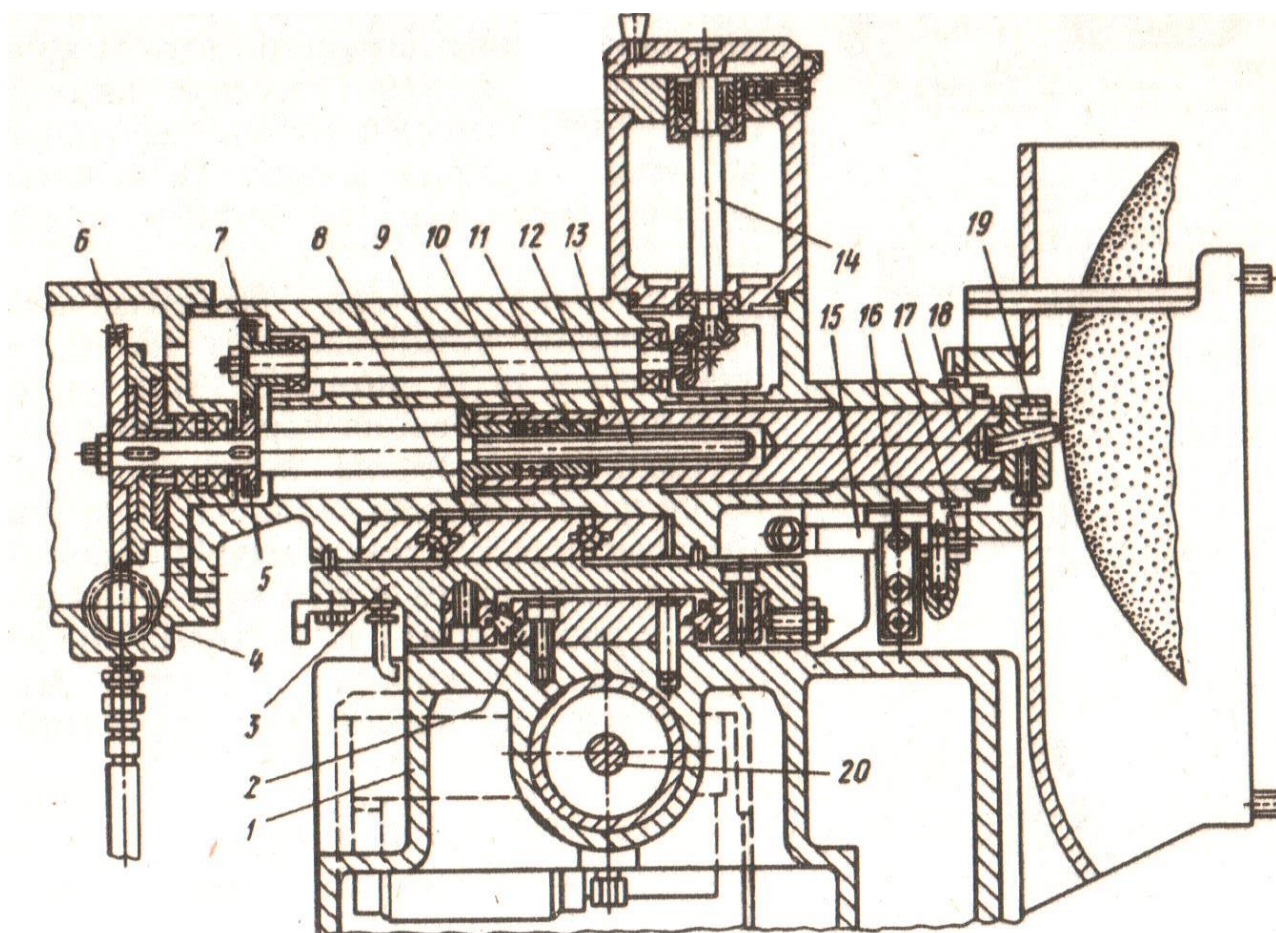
Прибор автоматической правки шлифовального круга станка 3М151
